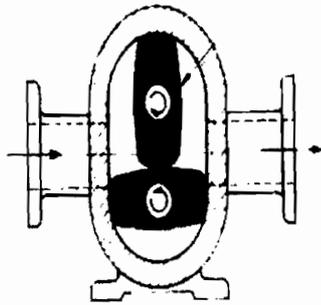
เครื่องสูบบแบบเฟืองภายใน Internal Gear Pump
